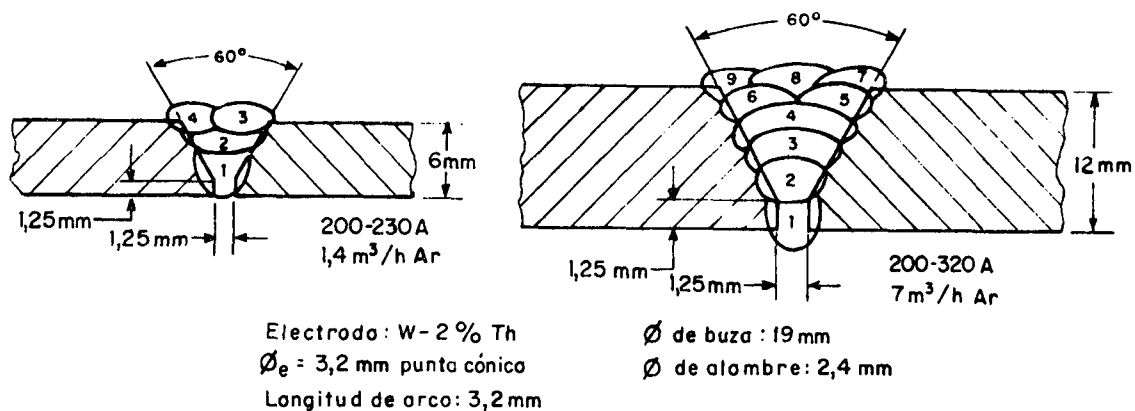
Procedimientos de soldadura GTAW en espesores de 6,3 y 12,5 mm.
